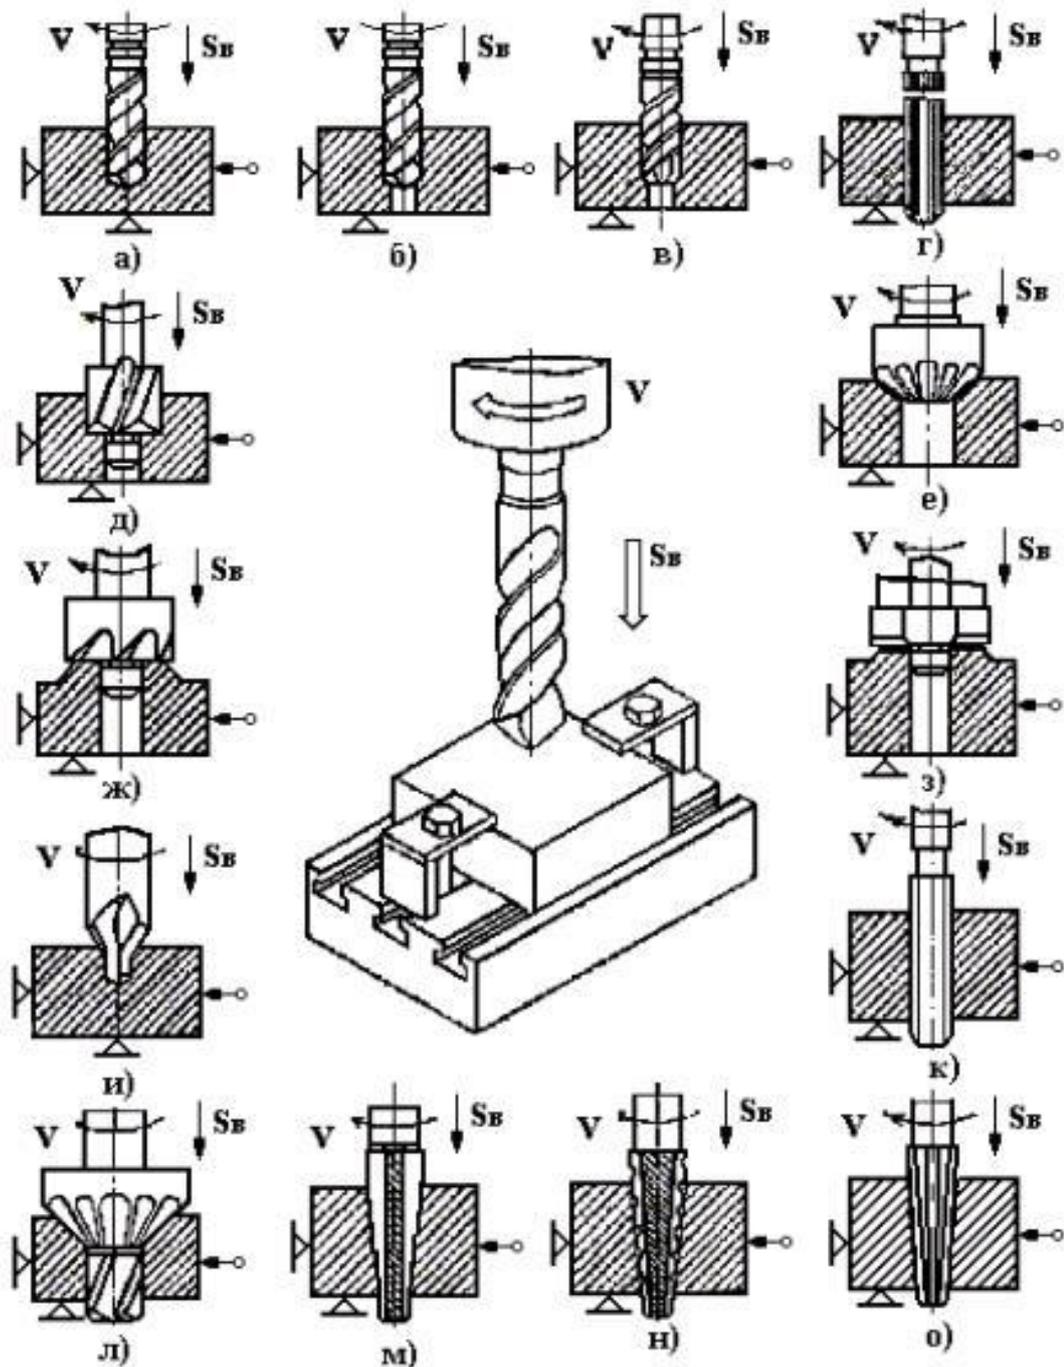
Схемы обработки поверхностей на сверлильных станках: а – сверление; б – рассверливание; в – зенкерование; г – развертывание; д – цилиндрический зенкер (зенковка); е – конический зенкер (зенковка); ж – цековка; з – пластинчатый резец; и – центровочное сверло; к – метчик; л – комбинированный инструмент; м – конический зенкер; н, о – конические развертки
